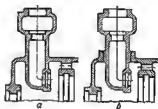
Construcciones completamente de fundición (a) y soldada-fundida (b)
